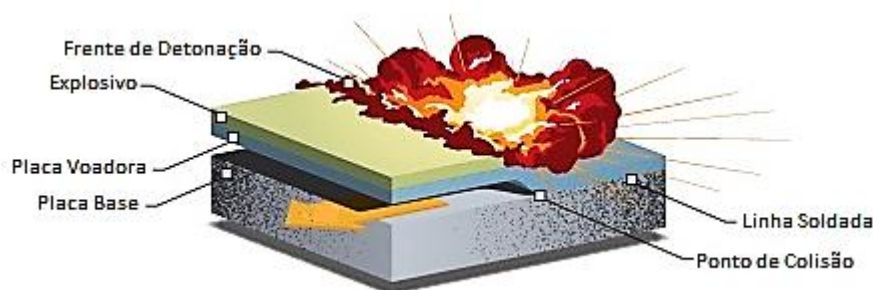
Processo de soldadura por explosão em placas paralelas.
